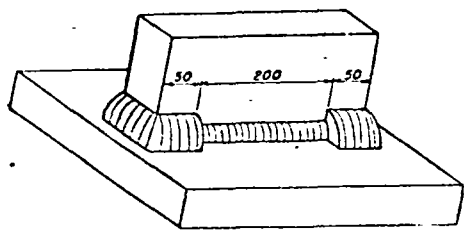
Ensayo de soldadura en ángulo embridado.
